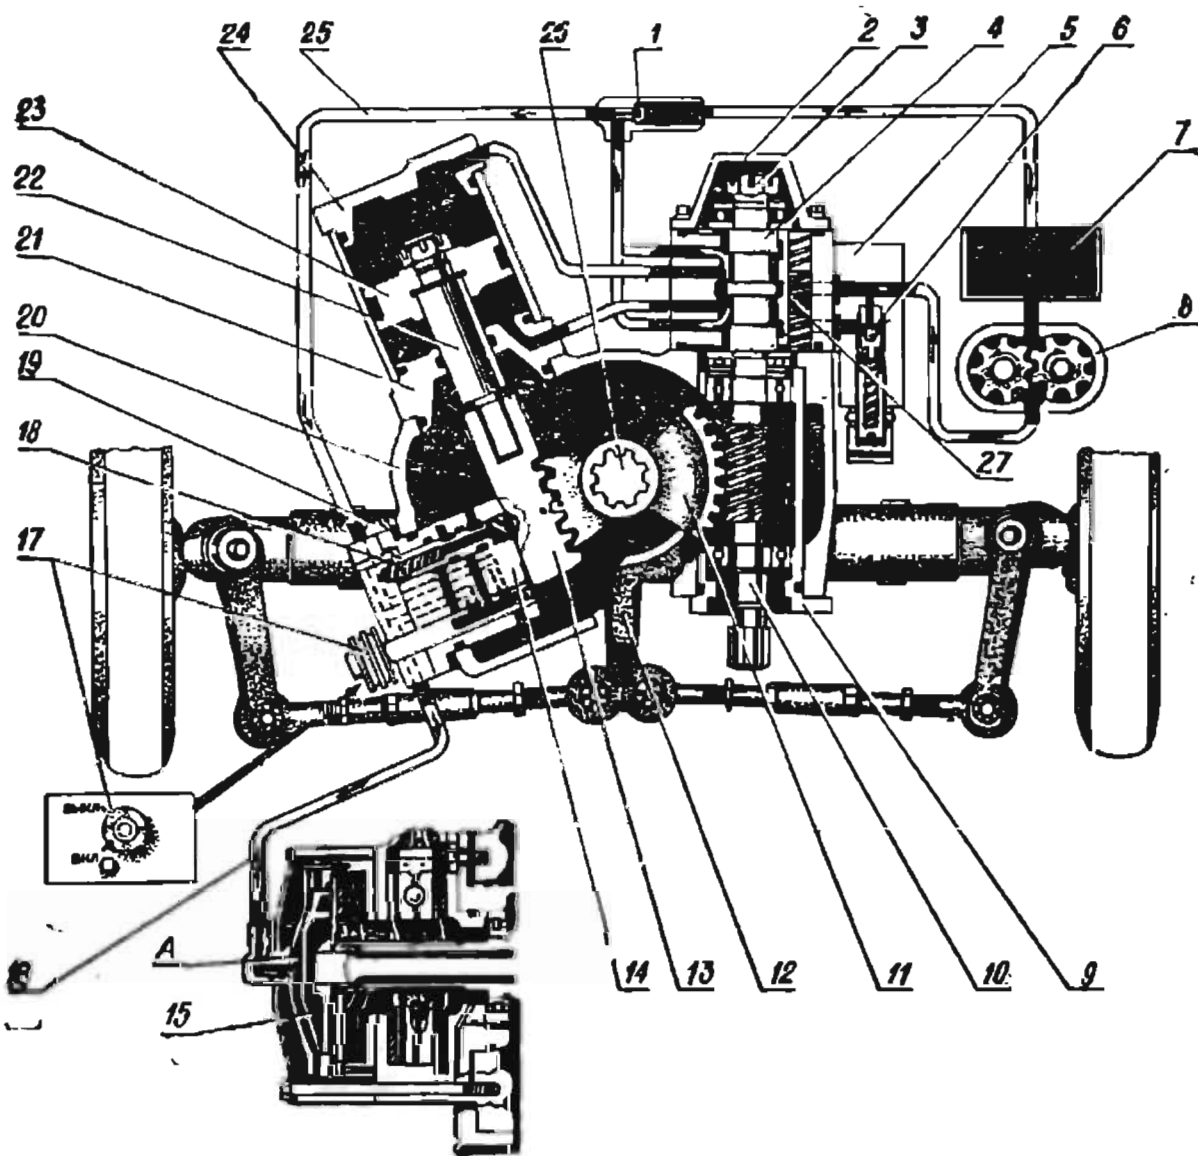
Схема гидроусилителя рулевого управления и блокировки дифференциала:
